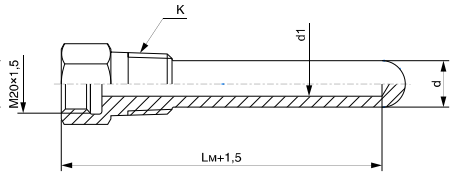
ГТ-712 цилиндрическая с конической резьбой для ДТ с неподвижным штуцером
